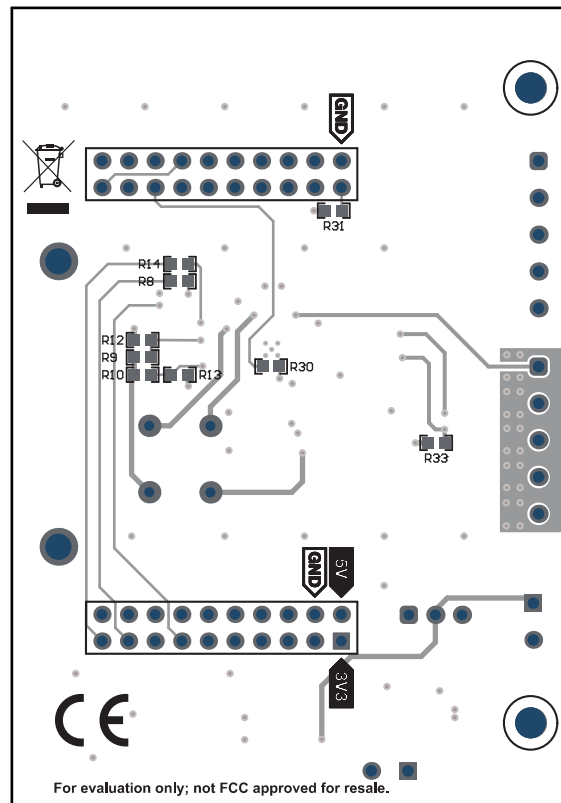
ADS122x14EVM 的 PCB 布局 (底视图)
